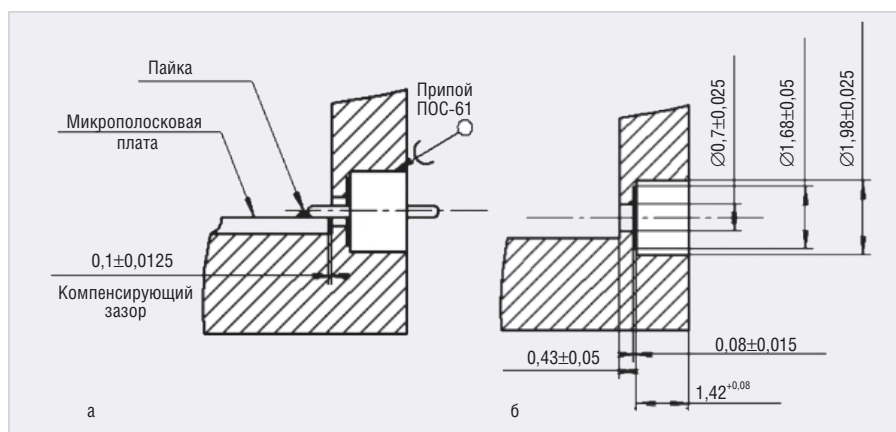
СВЧ-ввод МК100А: а) установка в корпус изделия; б) разделка корпуса под установку ввода
